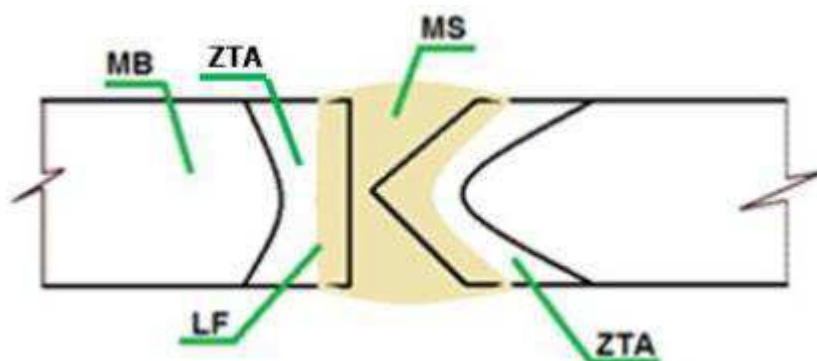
Diferentes regiões macroscópicas de uma junta soldada com passe único (Farias 2013).
